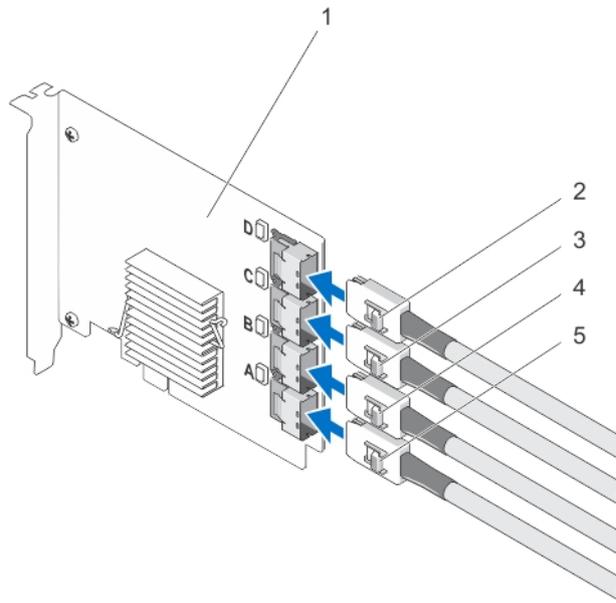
Cableado de una tarjeta del adaptador de extensión PCIe
